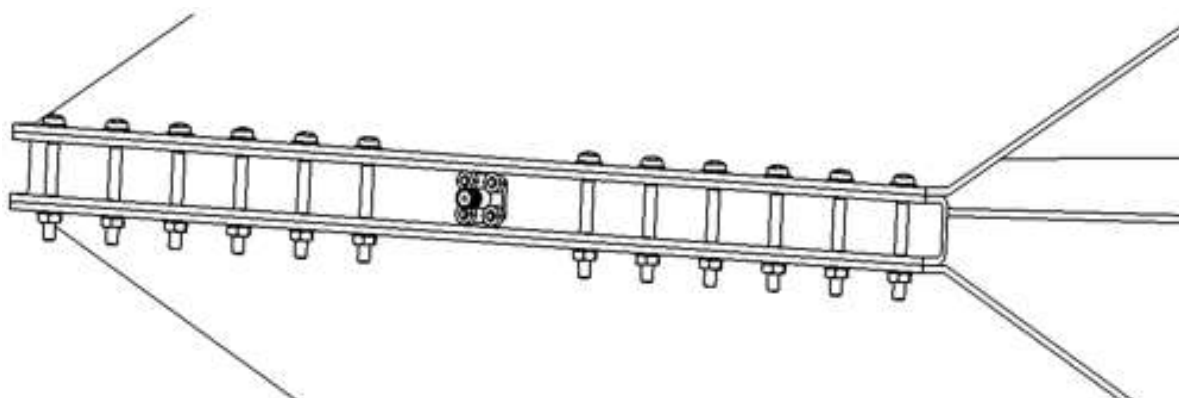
Винтовое соединение СВЧ-соединителей и корпуса ТЕМ-камеры к П-образным соединителям
